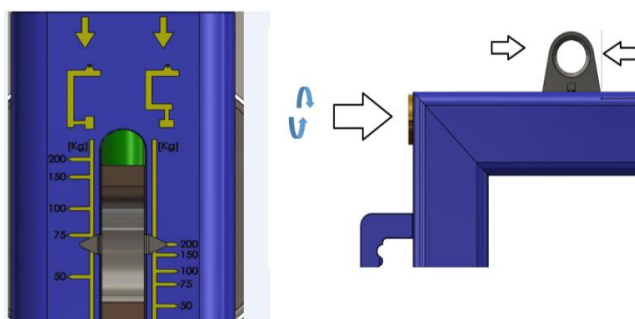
REGULAGEM POSICIONAMENTO DA BOBINA
